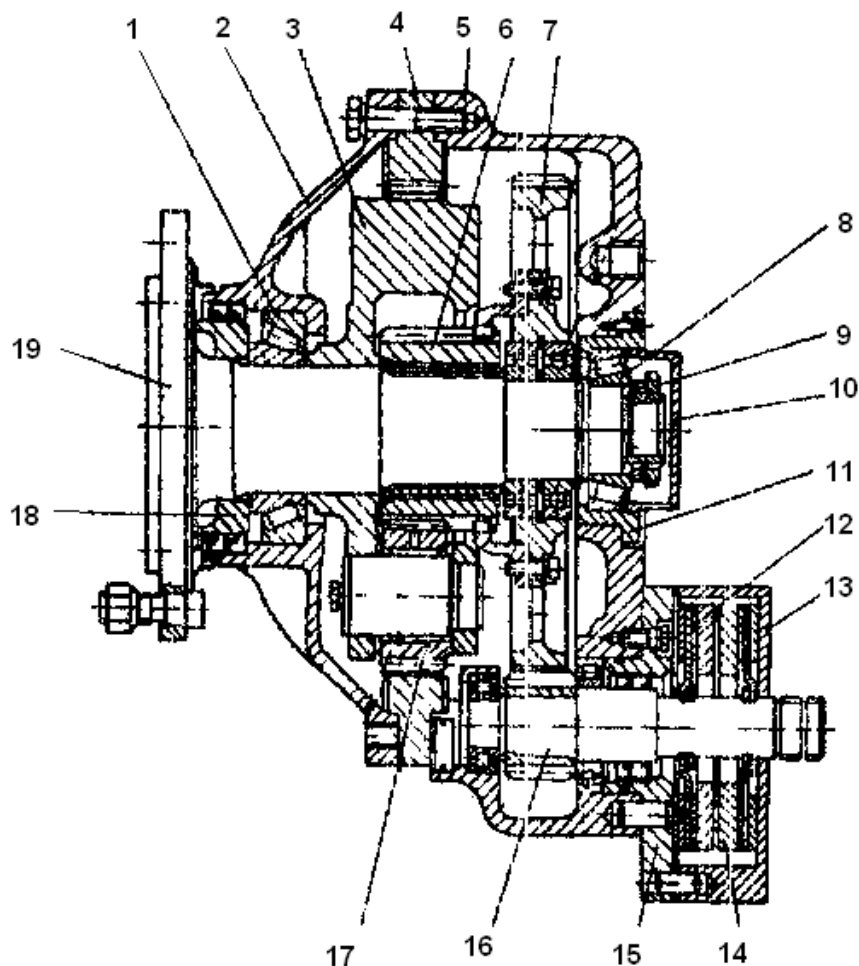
Бортовой редуктор (разрез): 1, 8 – подшипник оси; 2 – крышка; 3 – водило; 4 – коронная шестерня; 5 – корпус; 6 – солнечная шестерня; 7 – зубчатое колесо; 9 – гайка; 10 – крышка; 11 – стакан подшипника; 12 – фрикционный диск тормоза; 13 – корпус тормоза; 14 – нажимной диск тормоза; 15 – фланец; 16 – вал-шестерня; 17 – шестерня-сателлит; 18 – втулка уплотнений; 19 – ось ведущего колеса
